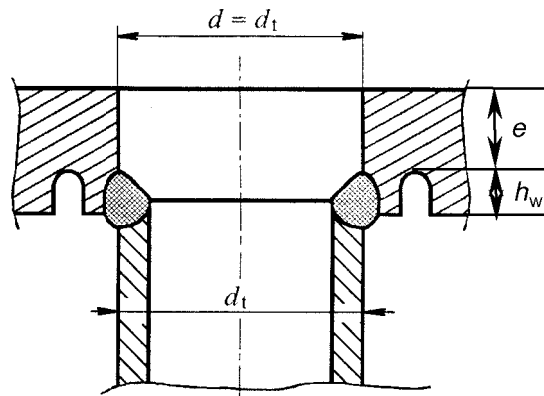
Tubo insertado soldado a la cara interior de la placa de tubos con ranuras mecanizadas
